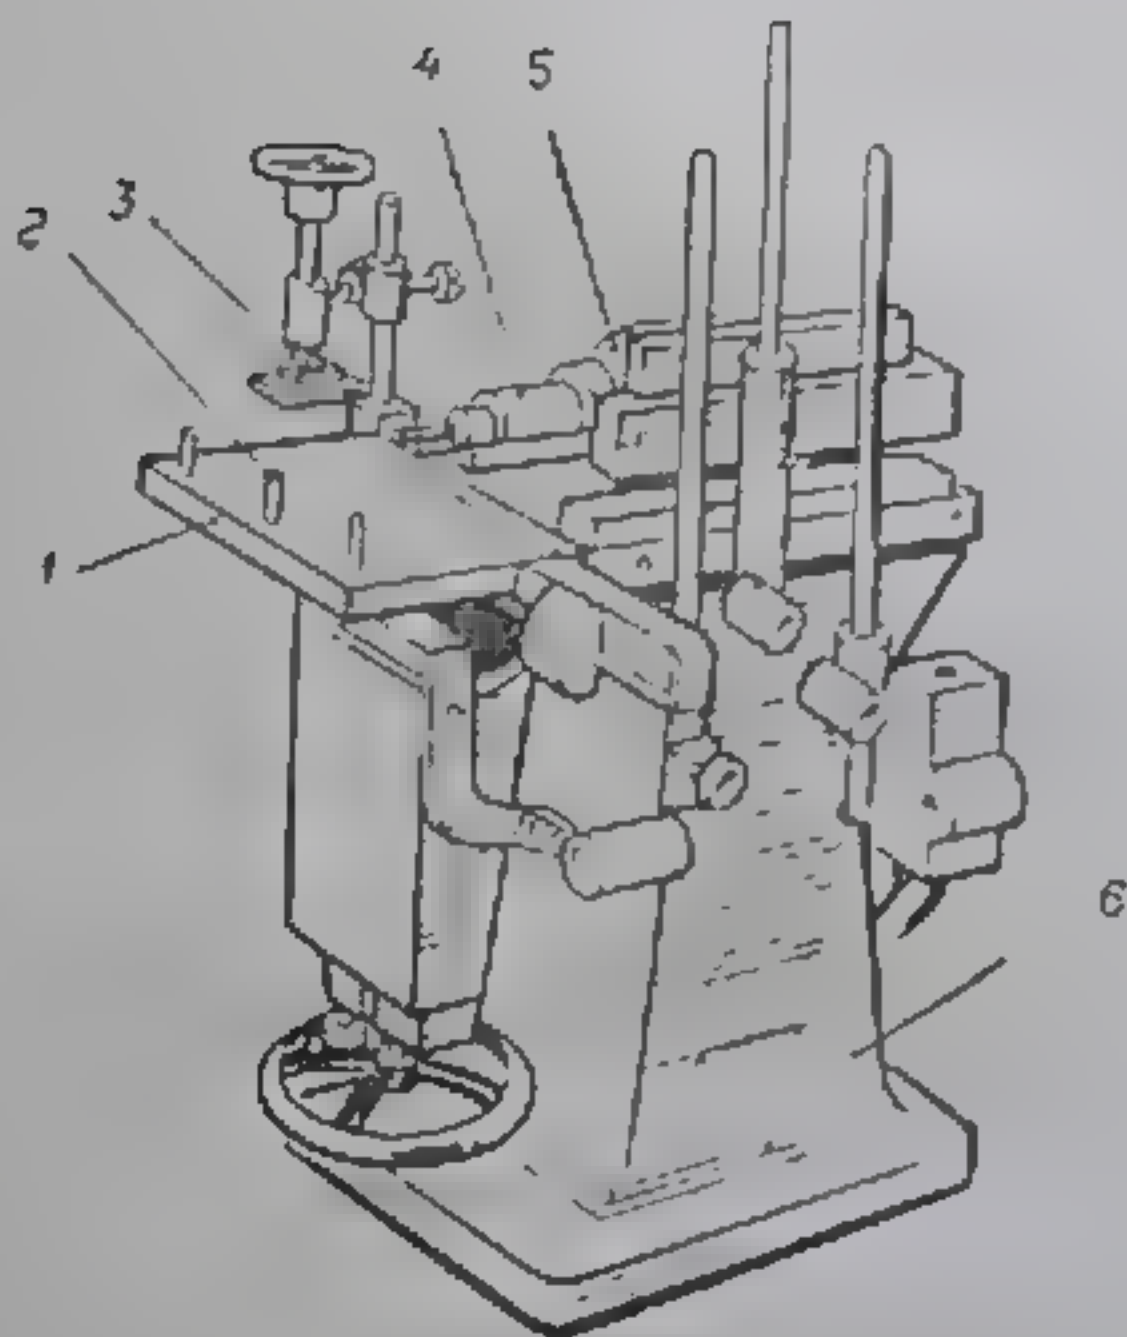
Горизонтальный сверлильно-пазовальный станок:
